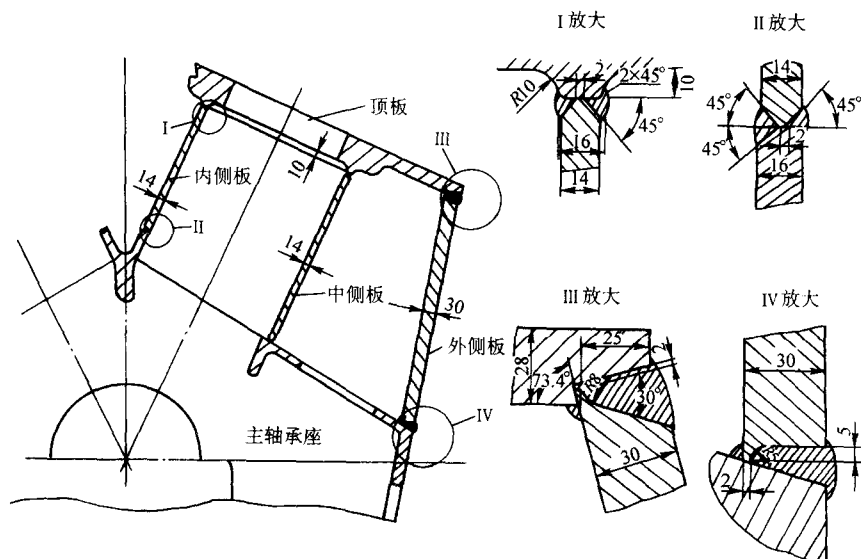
内、中、外侧板与主轴承座及顶板的焊接接头
